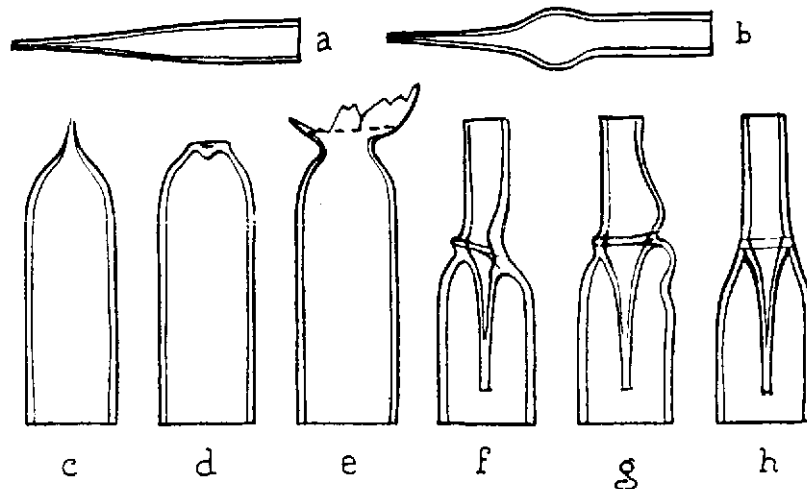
Double soudure ou ajustage intérieur.
